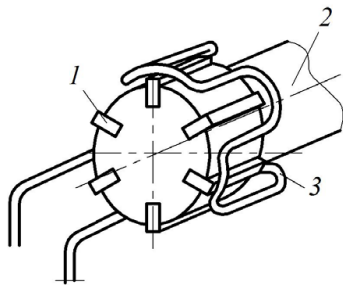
Установка индуктора для одновременной пайки режущих пластин многолезвийных инструментов:
